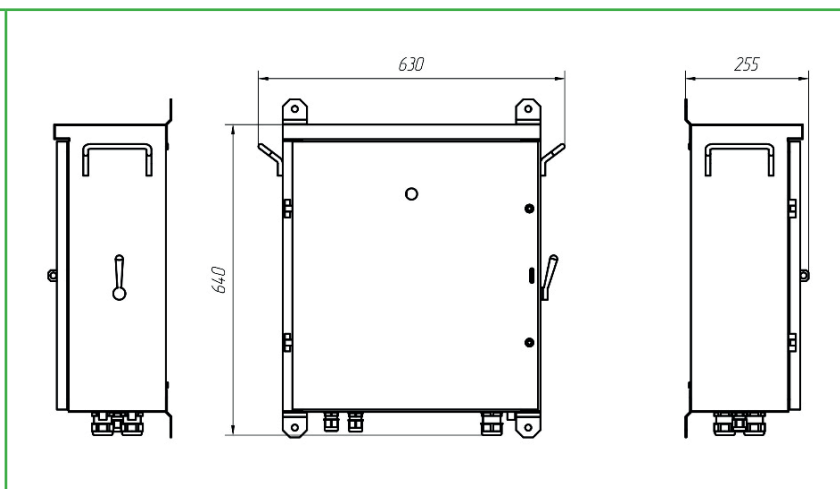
Конструкция РИП-LED-2-150 (250, 350, 400, 600)-36-1-УХЛ5
